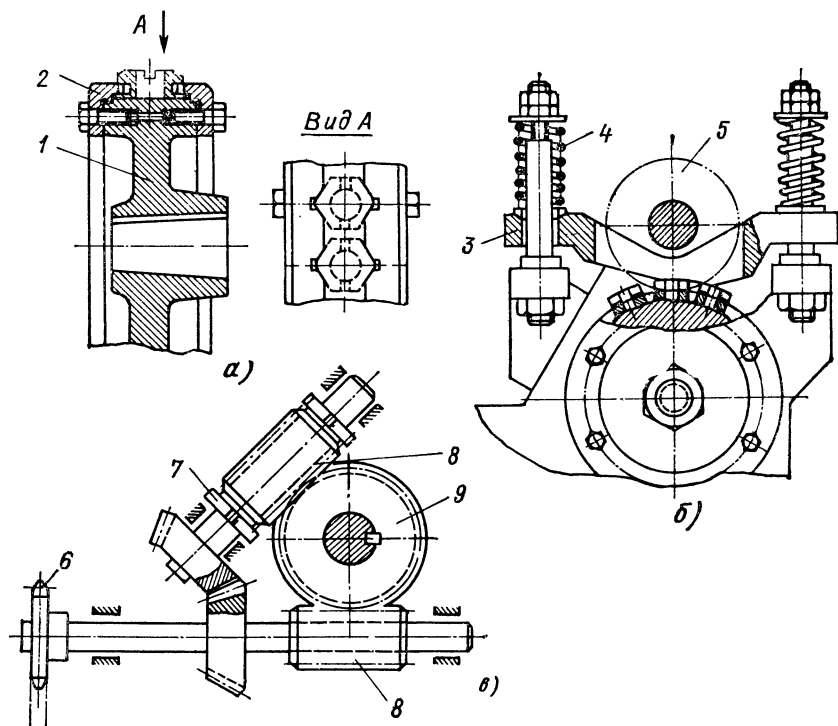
Схема автоматизации приспособления с горизонтальной осью вращения для непрерывного фрезерования шлицев корончатых гаек
